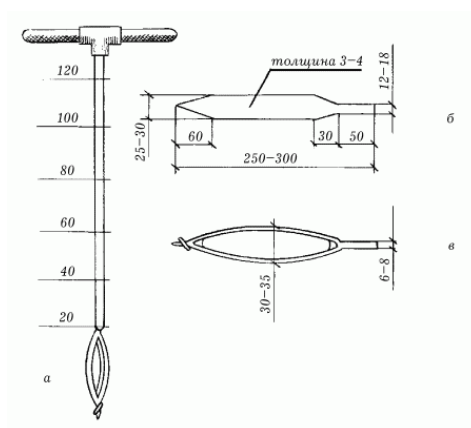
Почвенный бур: *а*– общий вид (в см); *б*– заготовка; *в* – головка бура.
